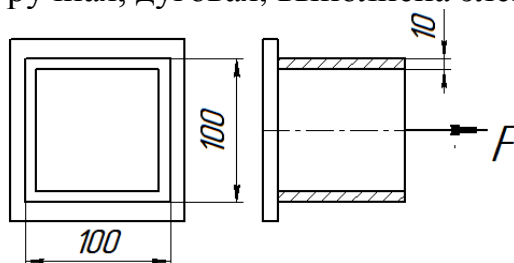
Сварное соединение трубы квадратного сечения, выполненное тавровыми сварными швами
